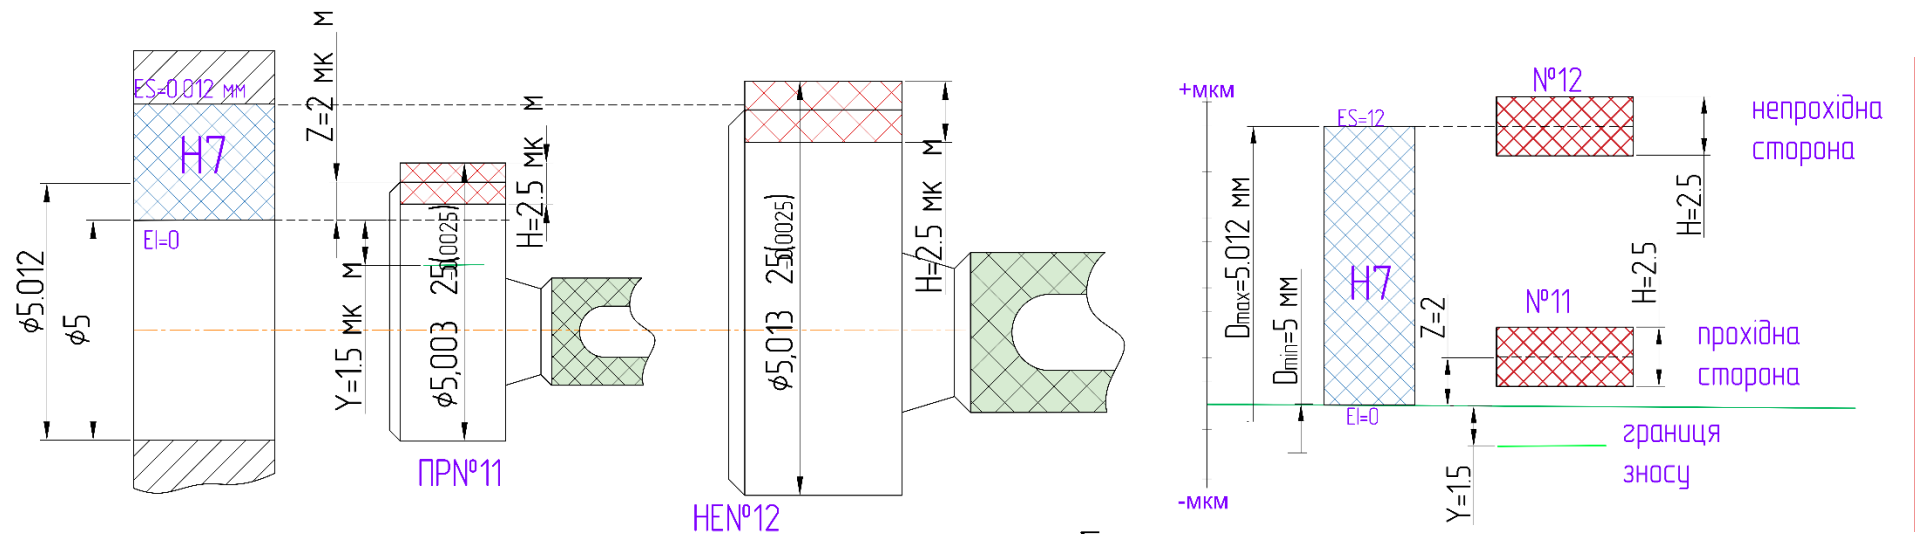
Повна схему розташування полів допуску калібру-пробки та деталі, що контролюється.
